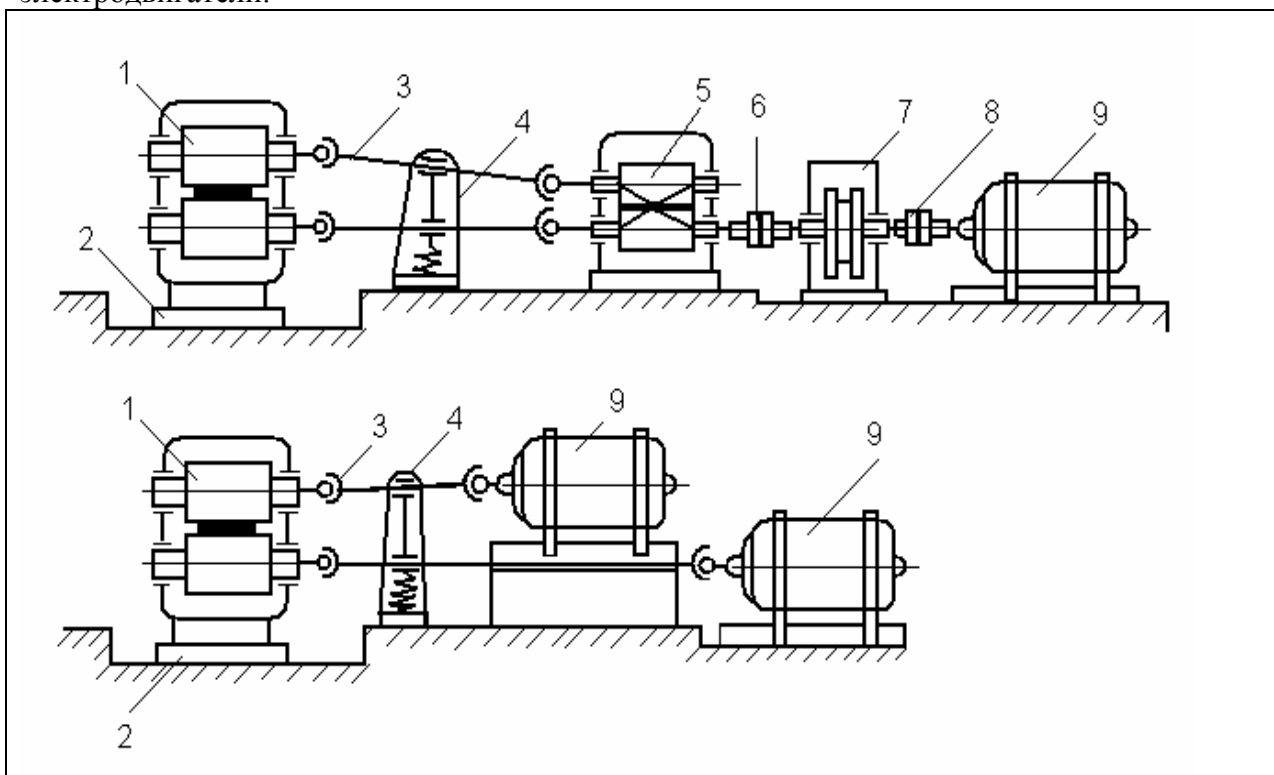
Схемы главных линий стана: а – привод валков через редуктор и шестеренную клеть; б – индивидуальный привод валков от главных электродвигателей: 1-валковый узел; 2-станина; 3- универсальные шпиндели; 4-устройство для уравнивания шпинделей; 5-шестеренная клеть; 6- коренная муфта; 7-редуктор; 8-моторная муфта; 9-главные электродвигатели
